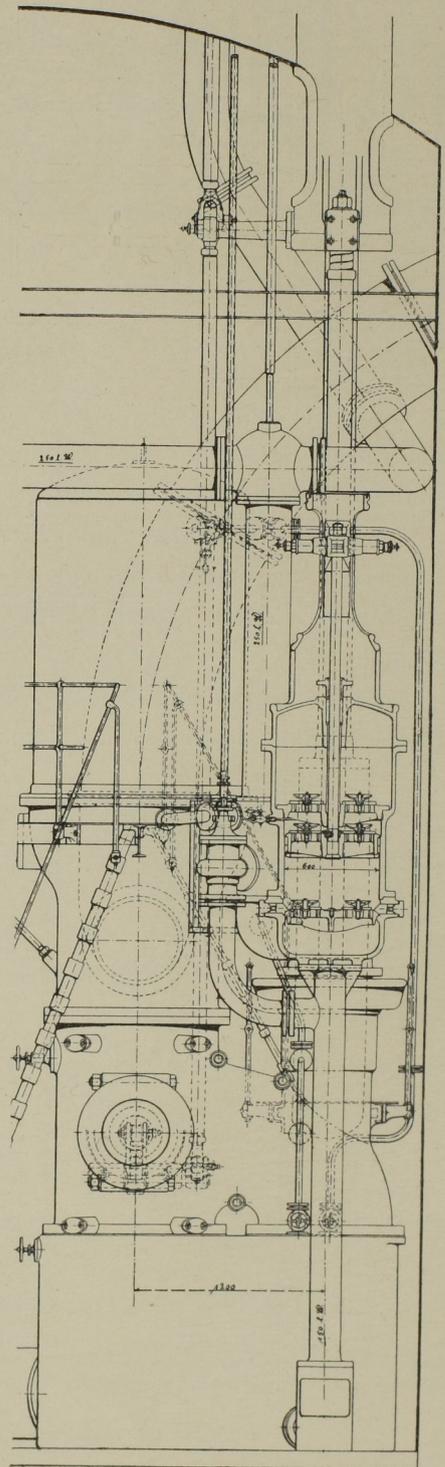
Seitenansicht der Druckpumpe und Luftpumpe.
